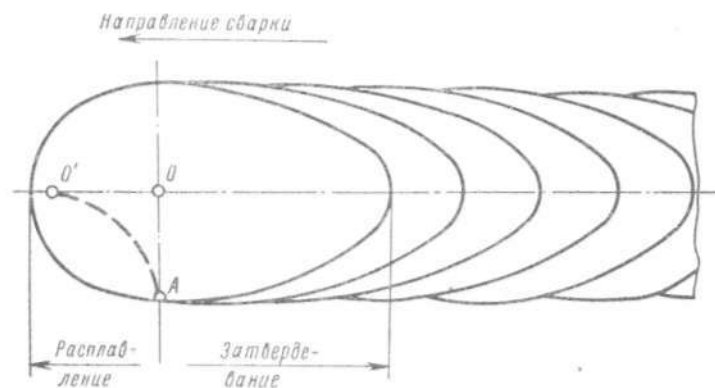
Схематическое изображение оси кристаллита, растущего при кристаллизации металла в условиях сварки.
